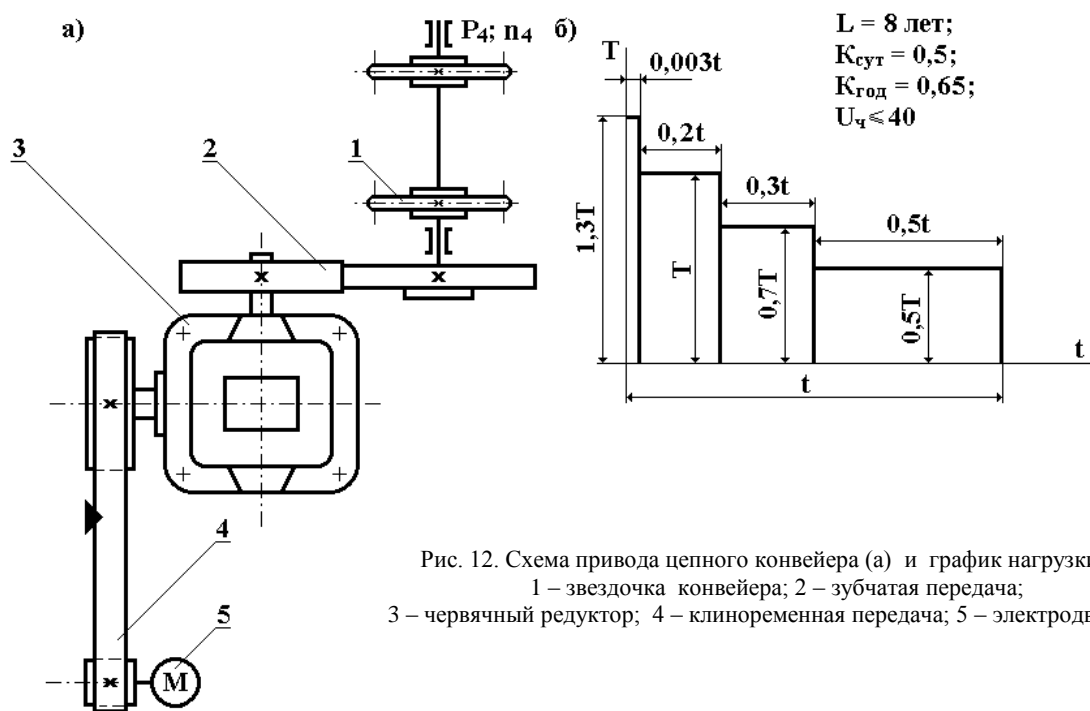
Схема привода цепного конвейера (а) и график нагрузки (б)
